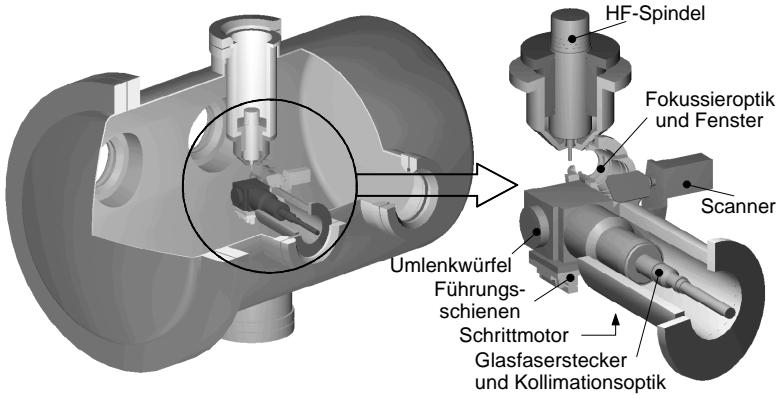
CAD-Skizze der aufgeschnittenen Kammer mit Komponenten zur Strahlführung
